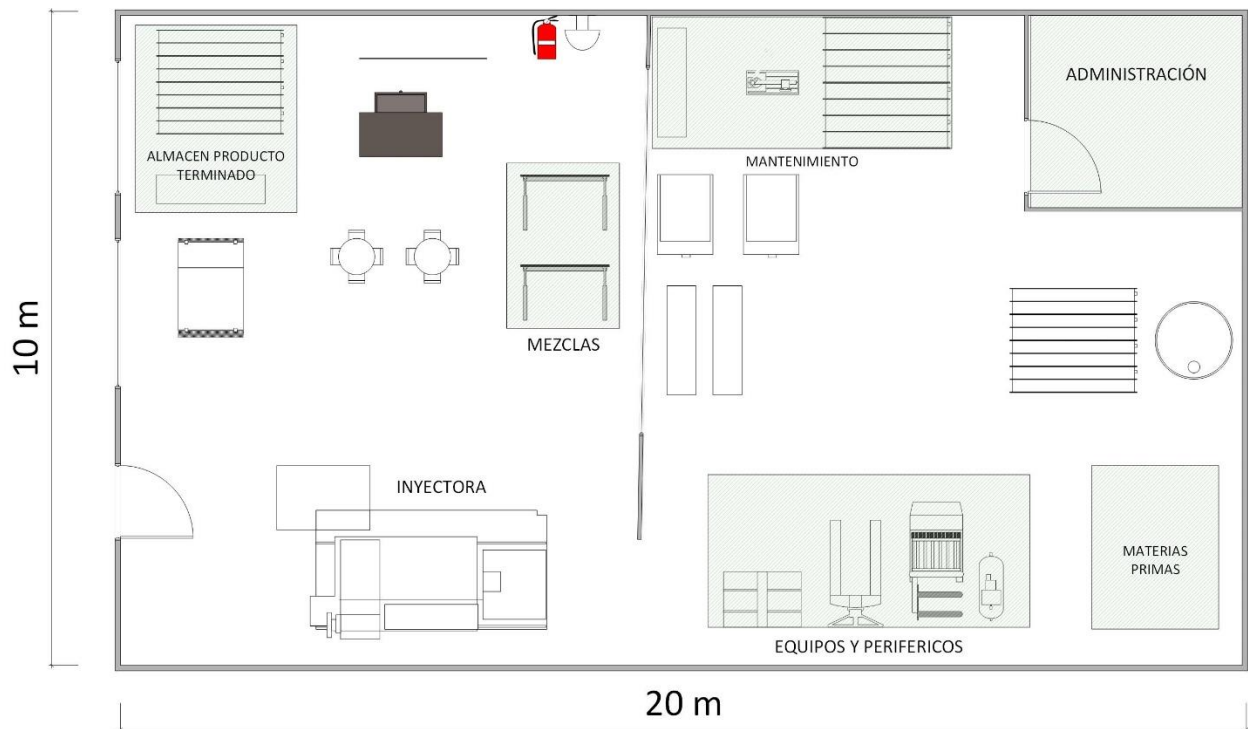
Plano distribución actual de la planta ambiente 108 SENA
